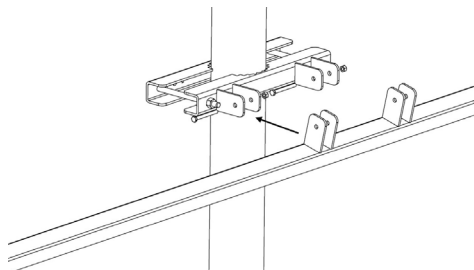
крепление рейки 5 к кронштейну для рейки 4
